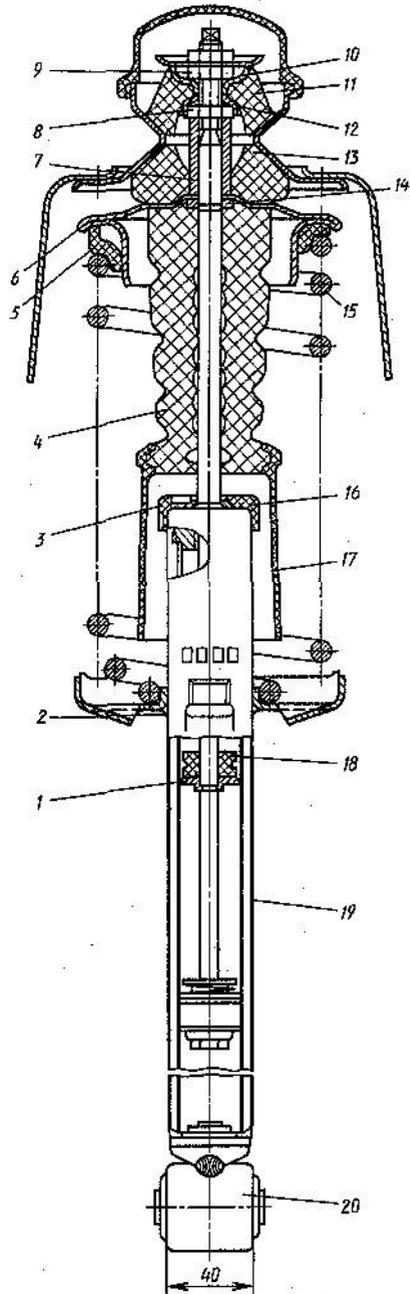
Дополнительный упругий элемент, изготавливаемый фирмой «Эластогран» из ячеистого полиуретанового эластомера «Целласто» и устанавливаемый на заднем амортизаторе с пружинной автомобиля «Фольксваген голф II». Свойства материала и форма элемента позволяют получить сильно прогрессивную характеристику упругости. При габаритной высоте 146 мм этот ячеистый элемент может быть сжат на 110 мм, воспринимая при этом усилие более 7 кН
